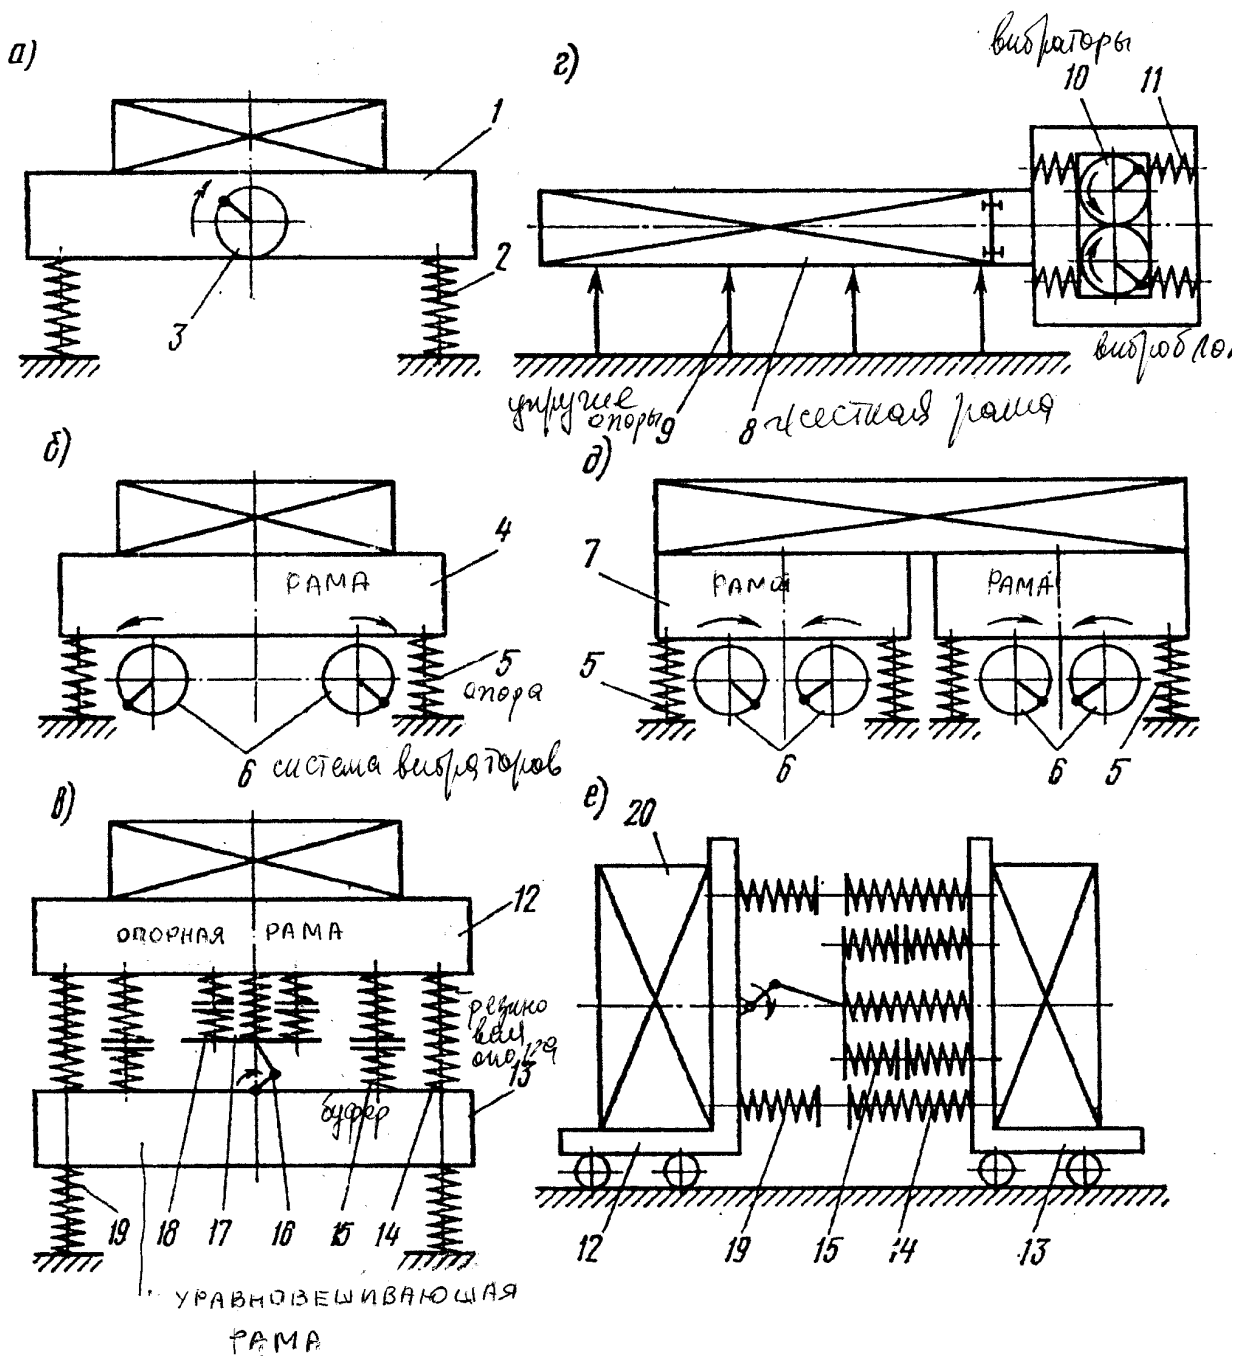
Схемы виброплощадок с различными видами колебаний: а - виброплощадка с круговыми гармоническими колебаниями; б — виброплощадка с вертикально направленными гармоническими колебаниями рамной конструкции; г - то же, блочной конструкции; д - с горизонтальными направленными гармоническими колебаниями; е - ударно-резонансная вертикальная; е - то же, горизонтальная.
